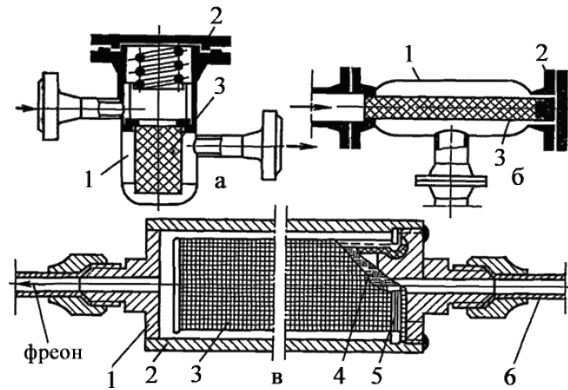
А,Б – грязеулавливатели: 1-корпус; 2- съемная крышка; 3- сетка; В- жидкостной фильтр. 1-крышка; 2 – обечайка; 3- латунная сетка; 4- асбест; 5- крепление фильтра к корпусу.
